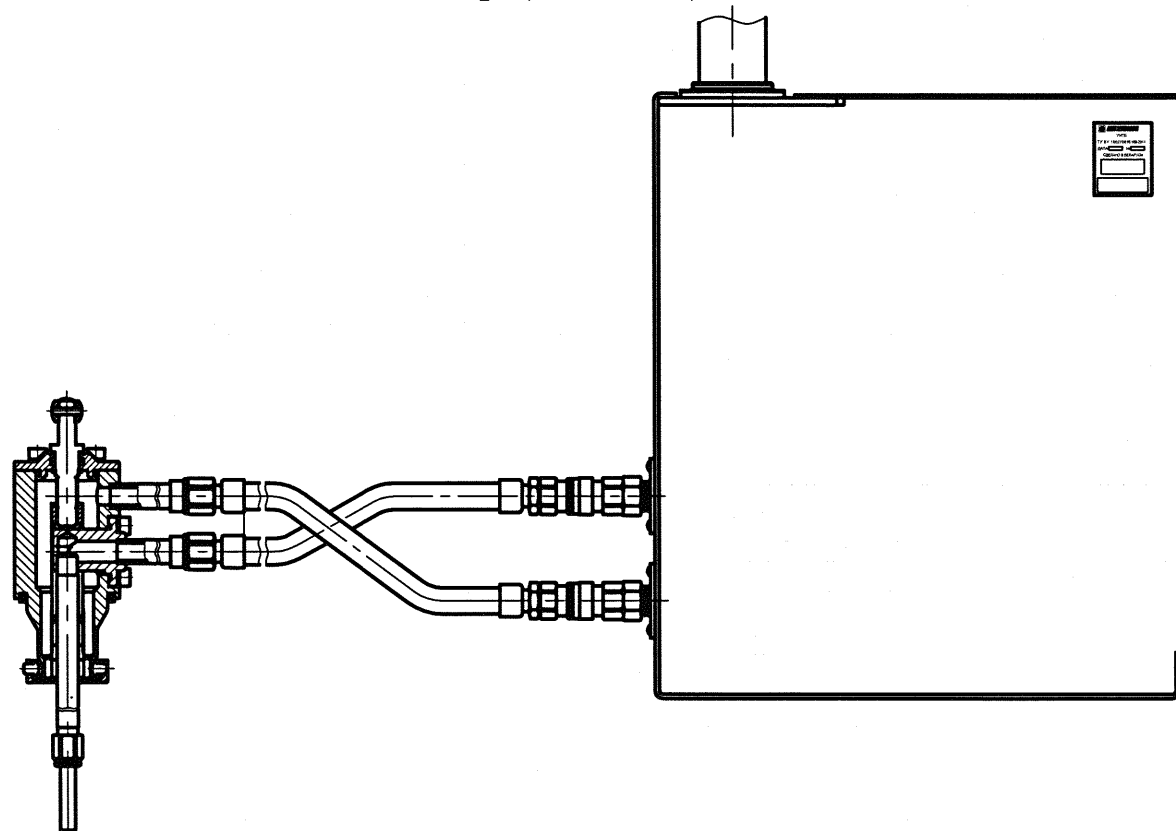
подключение струбцины для гидроиспытаний баллонов с наружным фланцем
